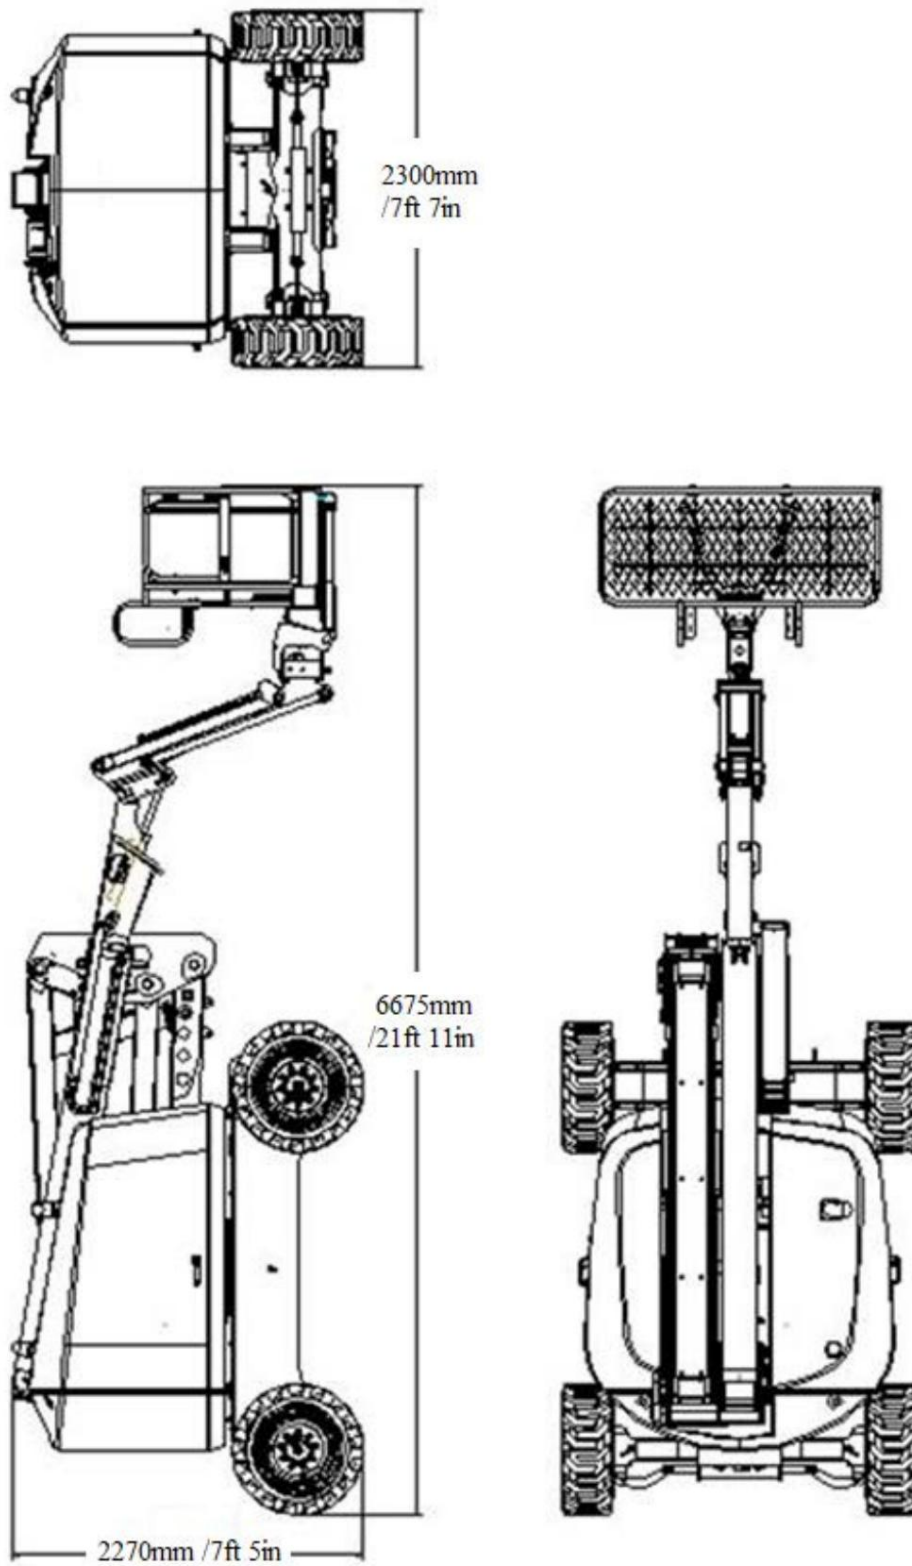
2 Dimensiunea ZA14j în modul de deplasare
